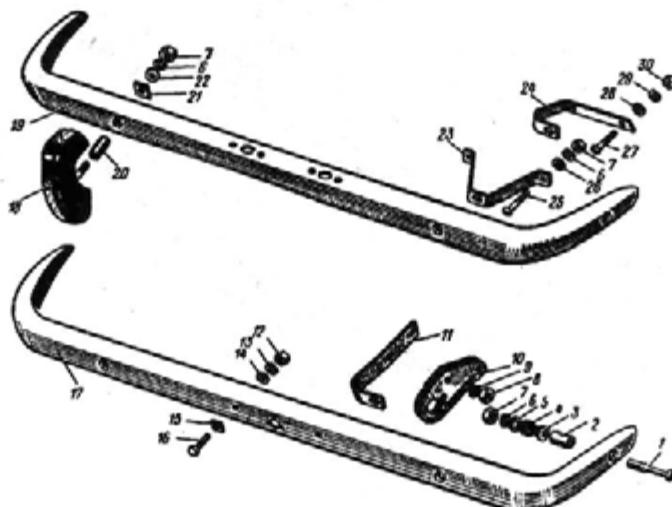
Передний и задний буфера с клыками и детали их крепления; детали крепления переднего номерного знака
